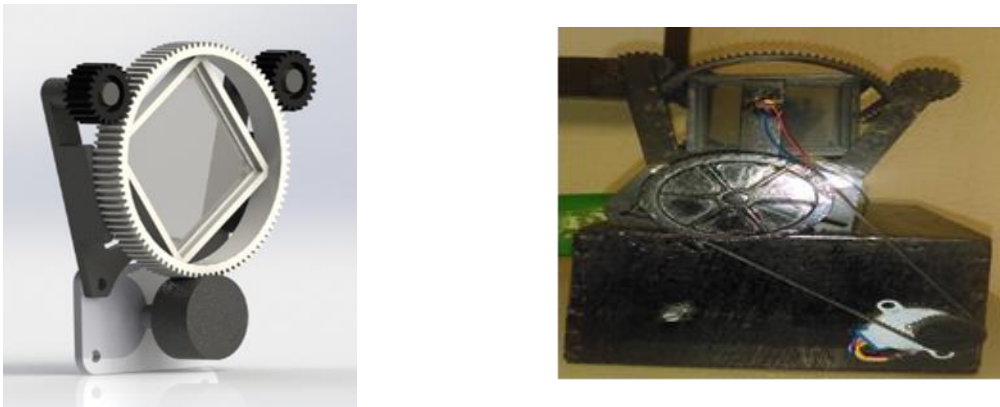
Ensamble de los 3 engranes de movimiento angular.
